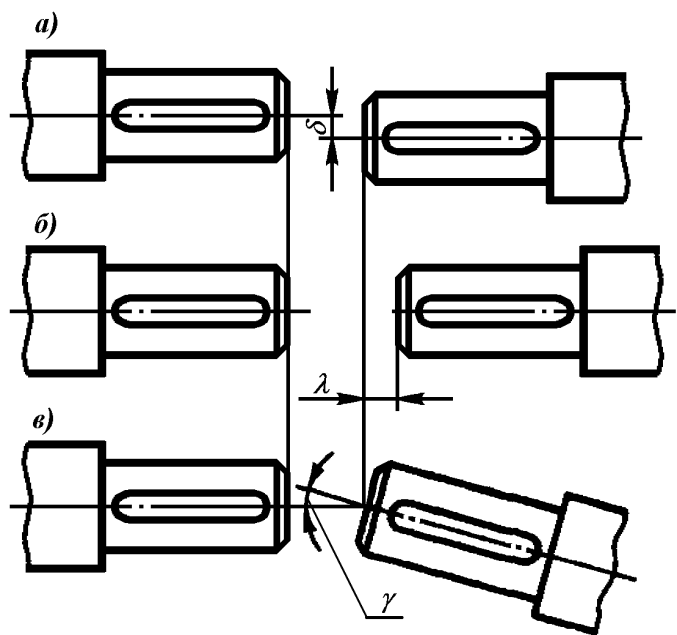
Виды относительного смещения соединяемых валов: а) радиальное (поперечное); б) осевое (продольное); в) угловое.
